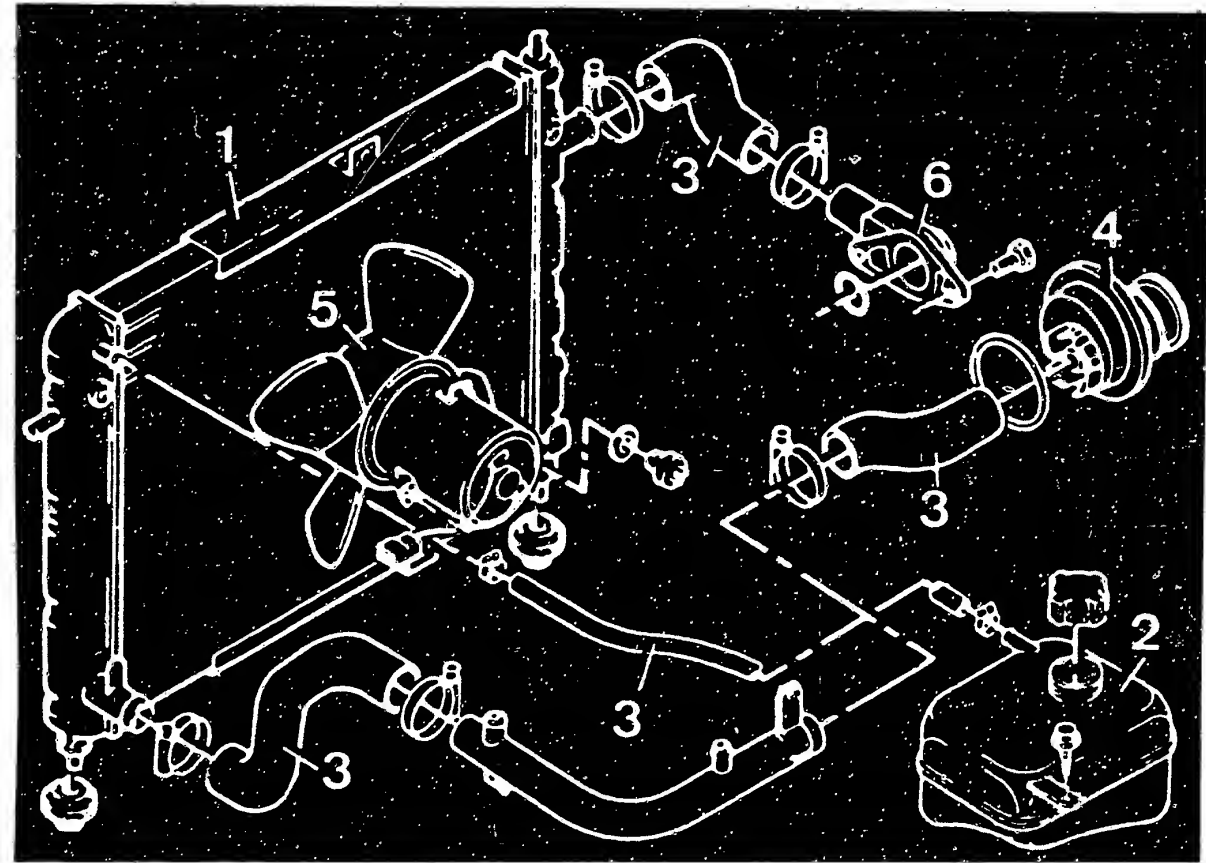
Die Elemente des Kühlsystems: 1 Kühler – 2 Expansionsgefäß – 3 Kühlerschläuche – 4 Wasserpumpe – 5 Elektrolüfter – 6 Thermostatgehäuse.
